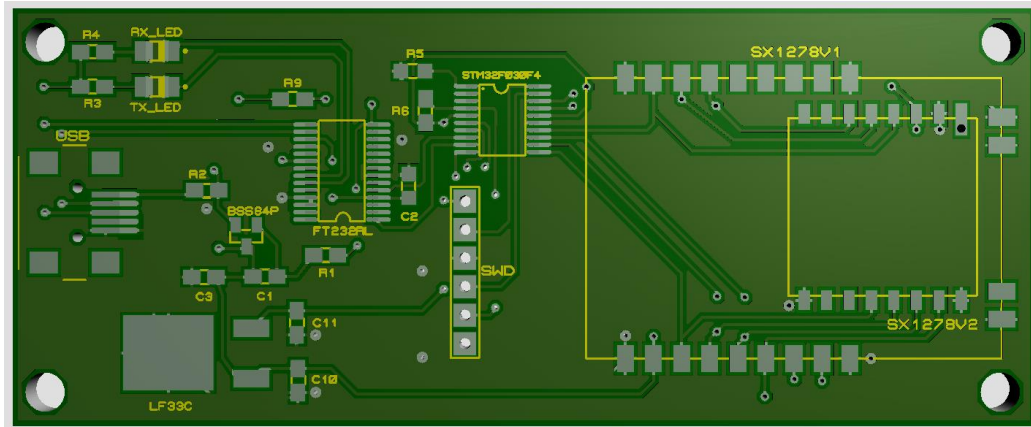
Versión final del diseño de la PCB de la estación receptora.
